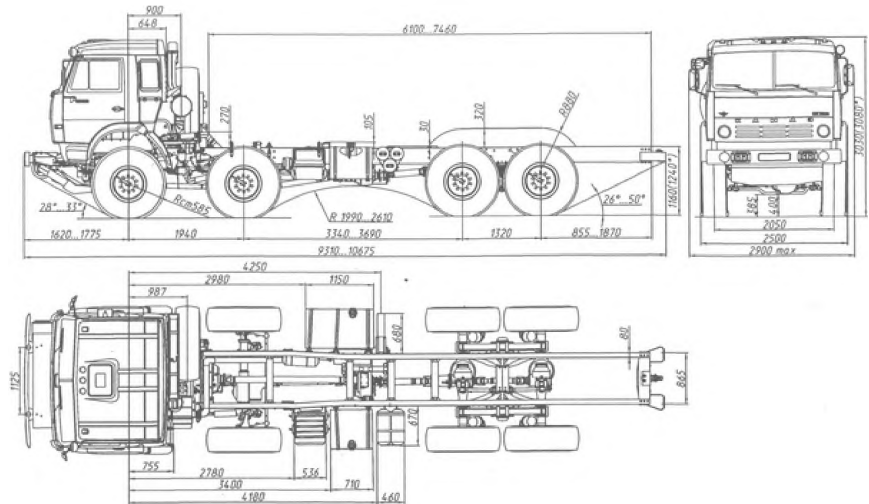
Шасси автомобиля-тягача КАМАЗ-63501. Габаритные размеры.
